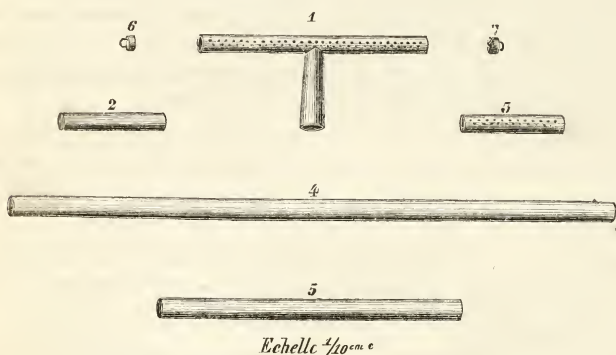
Tube-arroseur de M. Fabre-Bellanger.
